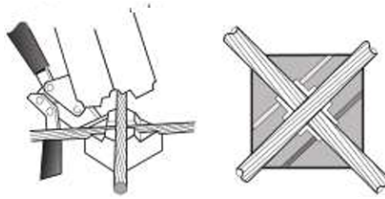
Introducir en el molde los cables a soldar según se muestra en la figura.
